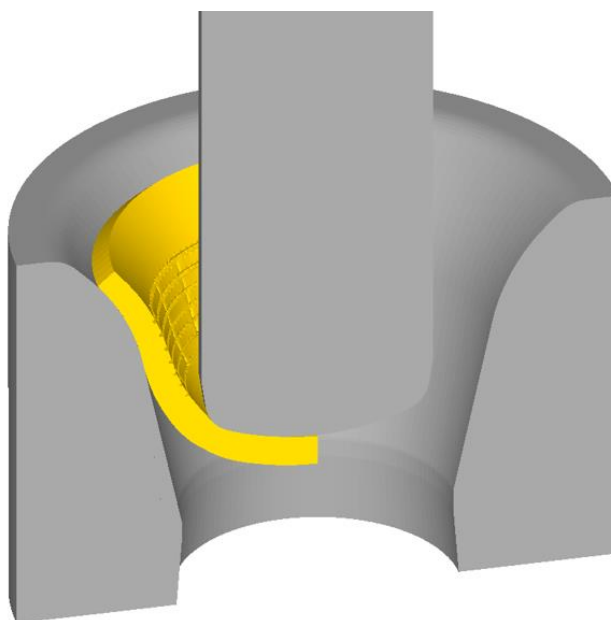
Моделювання витягування заготовки в 3D
